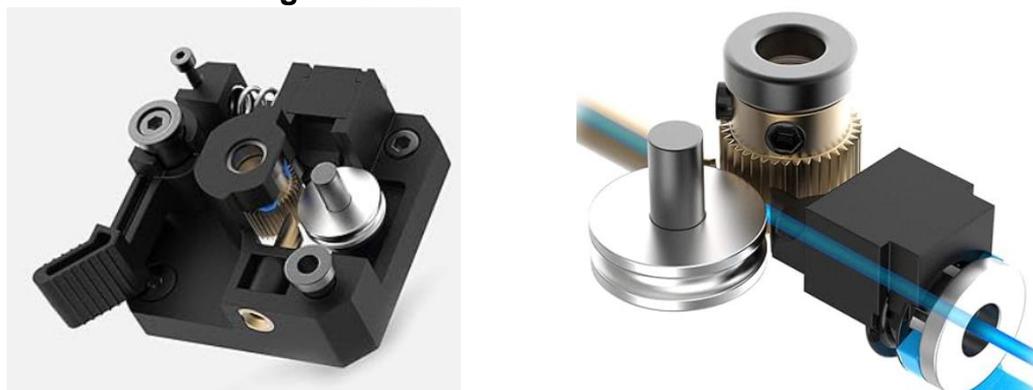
(a) Extrusora CR-6 desmontada e (b) Motor de passo Creality 42-40.
